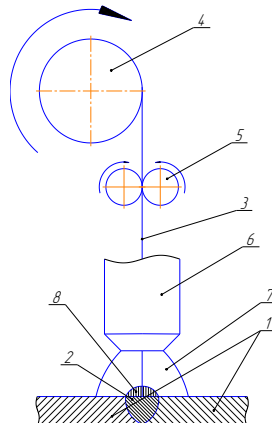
Схема напівавтоматичного зварювання у захисному газі
